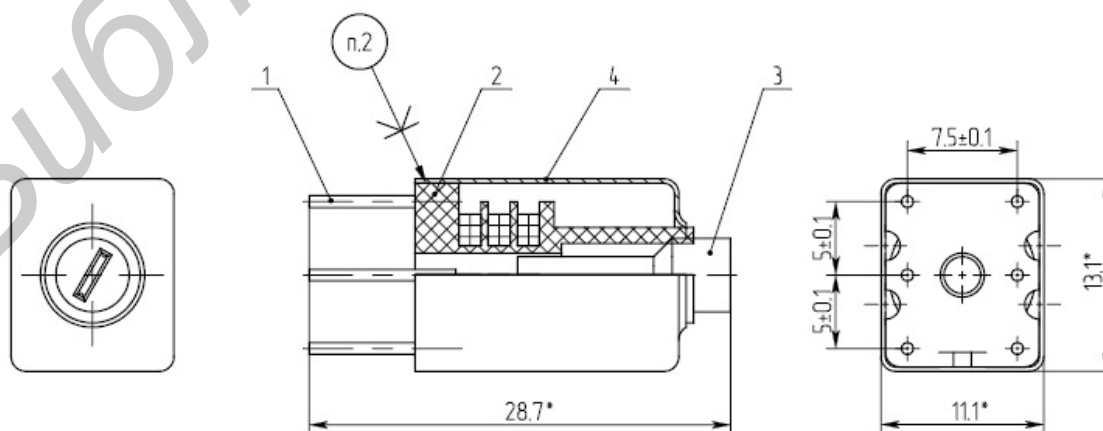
Вид сборочного чертежа катушки индуктивности
